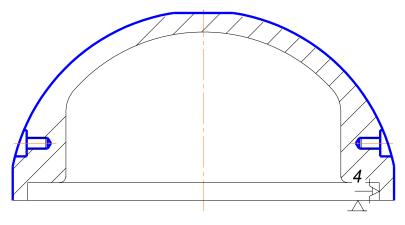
Схема базирования на 005 Токарной с ЧПУ операции
